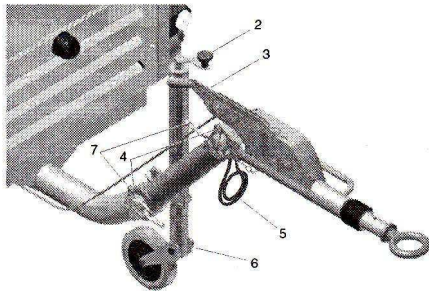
Einstellbare Zugstange mit Führungsrolle und Bremsen
